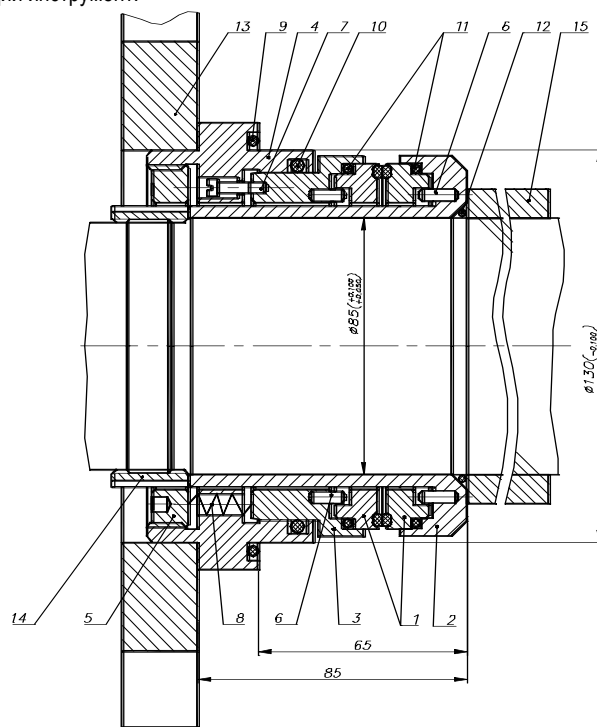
Торцовое уплотнение вала насоса: 1 – контактные кольца пары трения; 2 – гильза вала; 3 – аксиально-подвижная втулка; 4 – корпус уплотнения; 5 – гайка регулировочная; 6 – штифты; 7 – винт фиксатор; 8 – пружины; 9, 10, 11, 12 – резиновые уплотнительные кольца; 13 – прижимная обойма; 14 – гайка ротора; 15 – дистанционное кольцо
